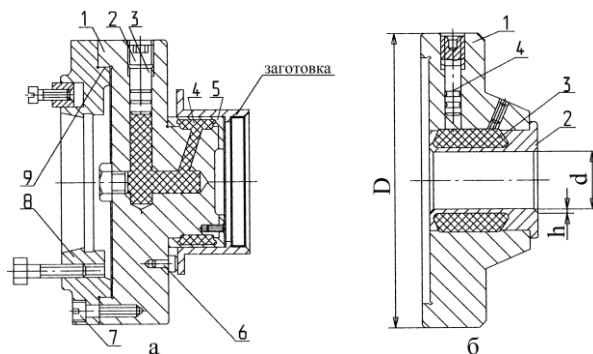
Конструкции приспособлений с гидропластмассой:
